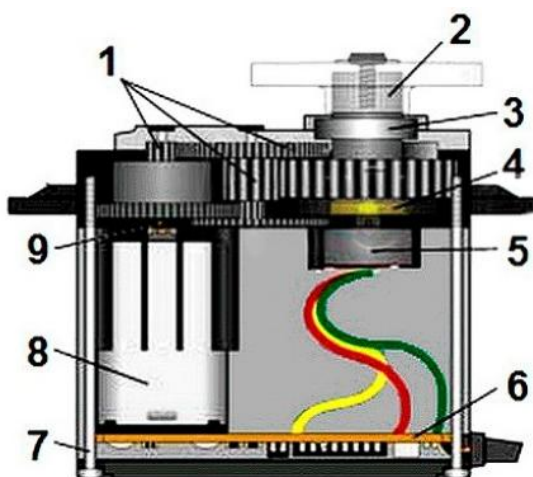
Конструкція сервопривода з металевим редуктором та системою зворотного зв'язку
